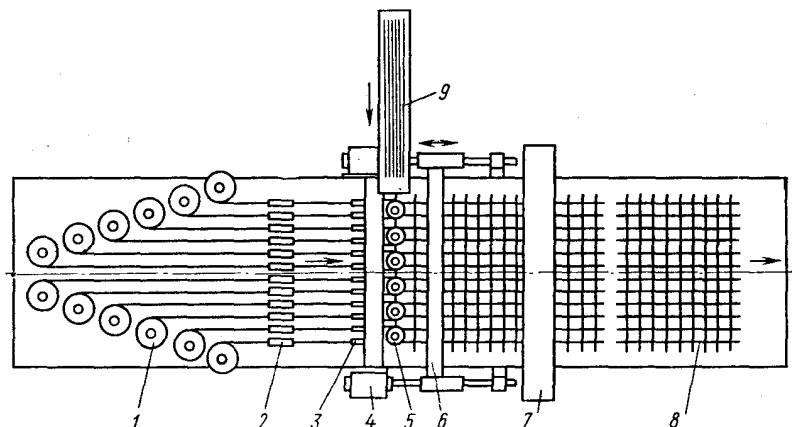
Схема автоматической установки для изготовления арматурных сеток
